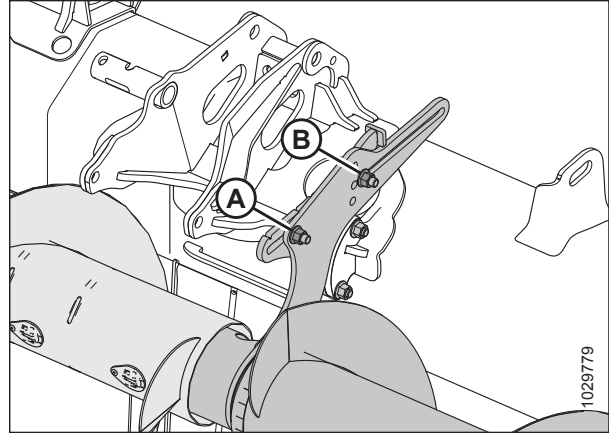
Ursprüngliche Einbaustellung – dreiteilige Schnecke
